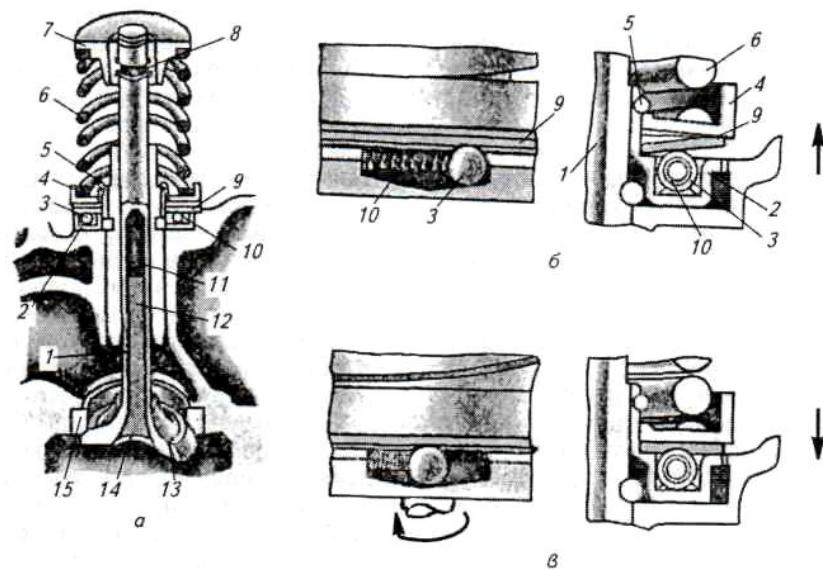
Выпускной клапан в сборе механизма газораспределения двигателя ЗИЛ:
